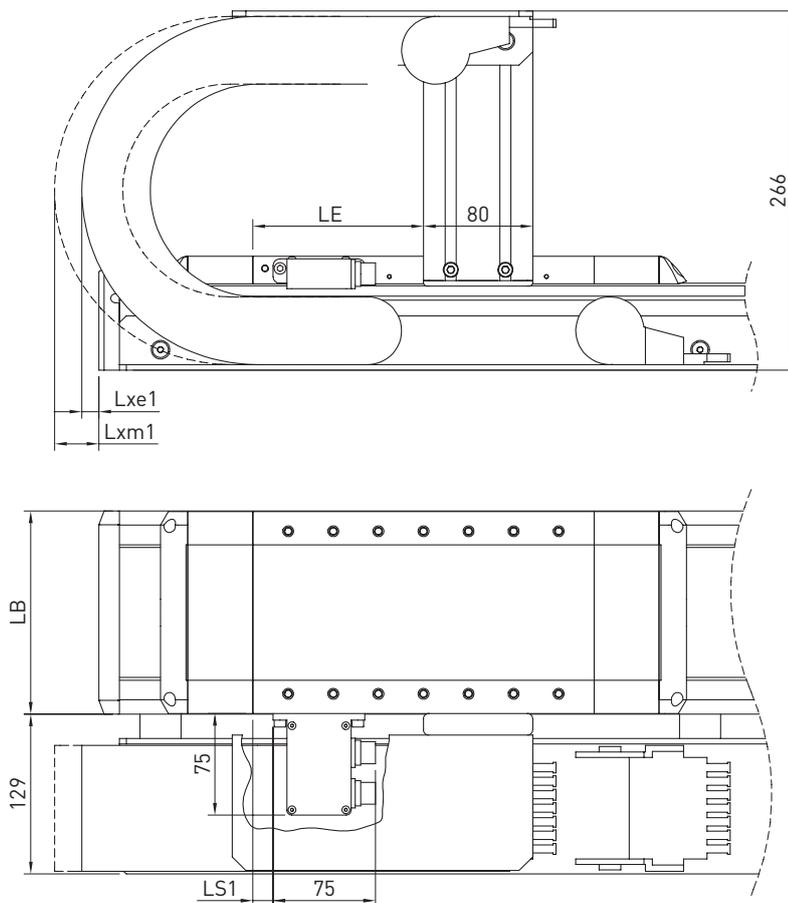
Linearmotorachsen HT-L: Option „D“ und „F“ – Stecker rechts/hinten, gilt gespiegelt auch für Option „C“ und „E“ – Stecker links/hinten
